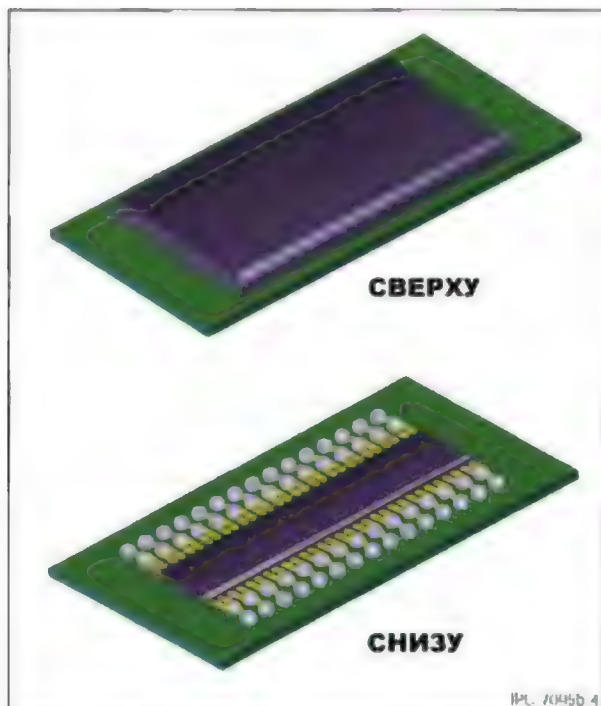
Верхняя часть литого корпуса BGA типа BOC
